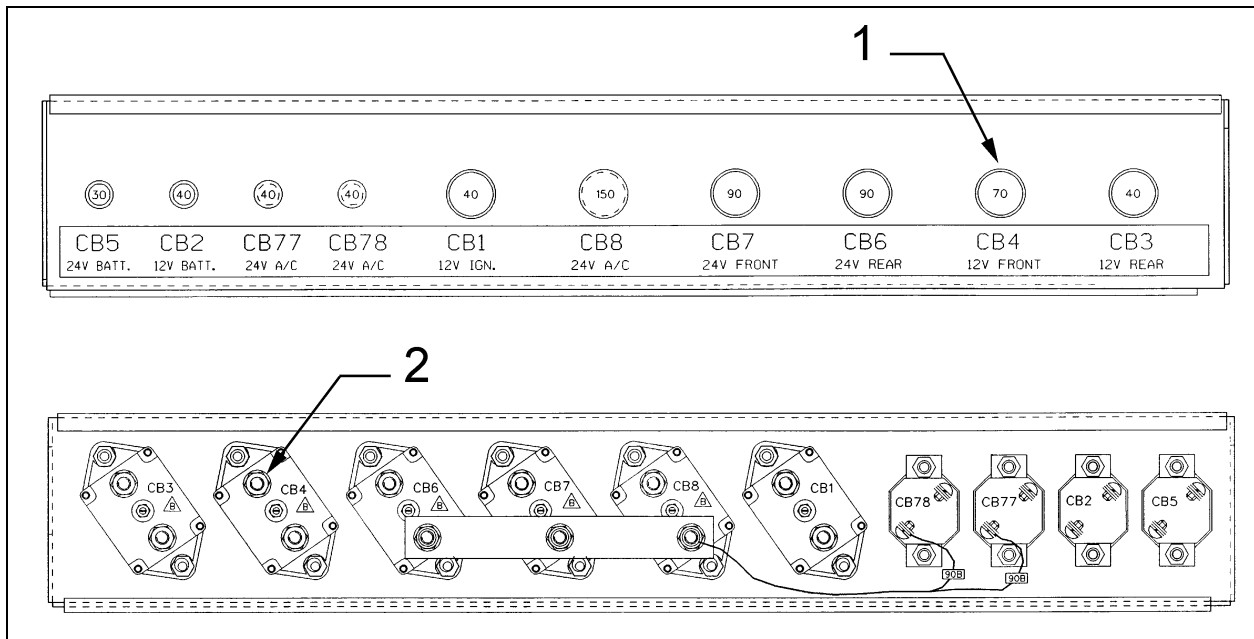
(1) Vue de face du disjoncteur CB4 ; (2) Vue arrière du disjoncteur CB4.
